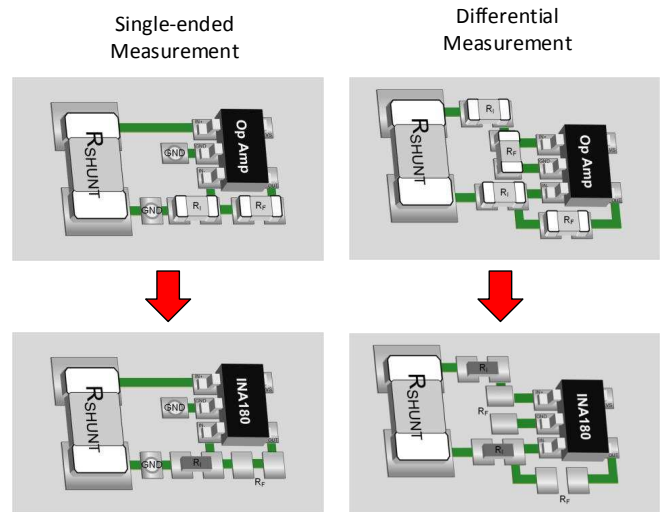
分立式解决方案到 INA180 PCB 的迁移技术
